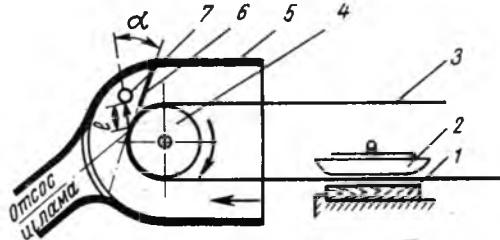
Схема устройства для непрерывного обдува шлифовальной шкурки сжатым воздухом:
